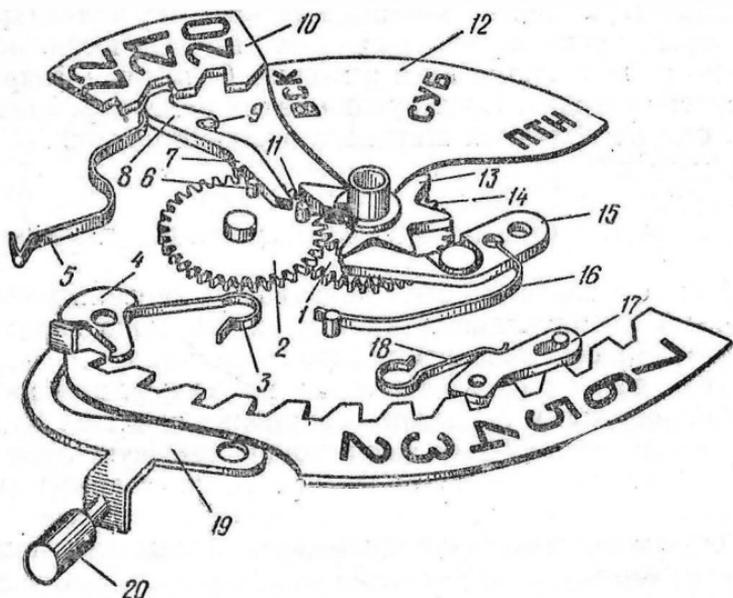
Кинематическая схема двойного календарного устройства часов 2627Н «Полет»:
